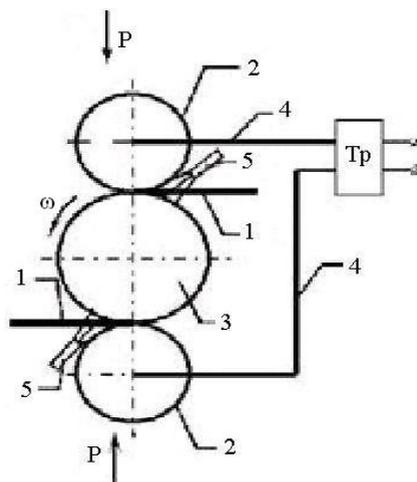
Схема электроконтактной наварки проволоки или ленты: 1 – проволока (лента); 2 – электродные ролики; 3 – деталь; 4 – вторичный контур сварочного трансформатора; 5 – подача охлаждающей жидкости
